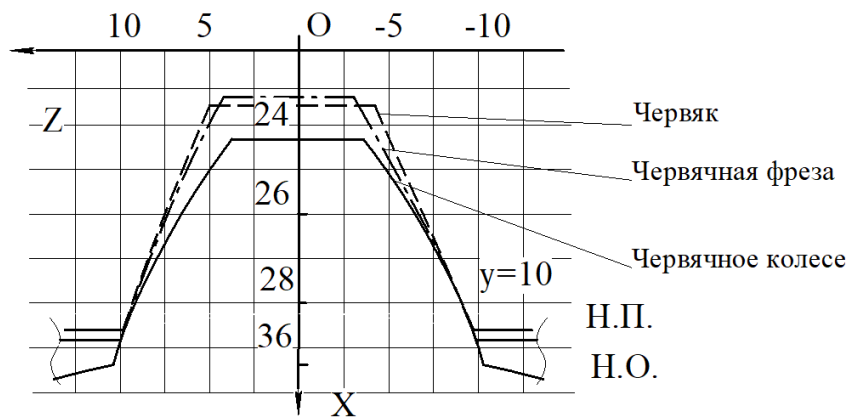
Профили червяка, червячной фрезы и червячного колеса в сечении $y=10$
